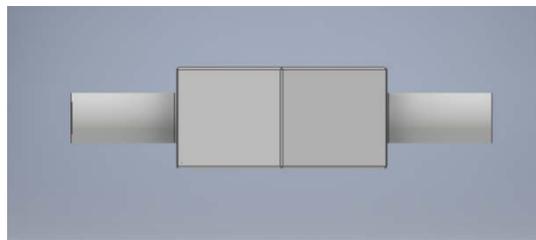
Cetakan Paving Block Prisma Segi 6 Tampak Atas
